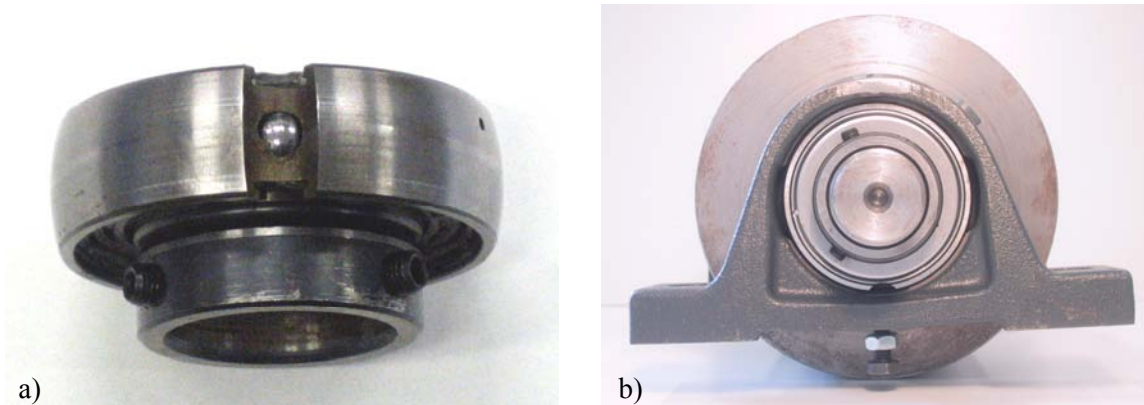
a) Mittels Drahterosion erzeugter Außenringschaden, Öffnungsdurchmesser 5,4 mm
